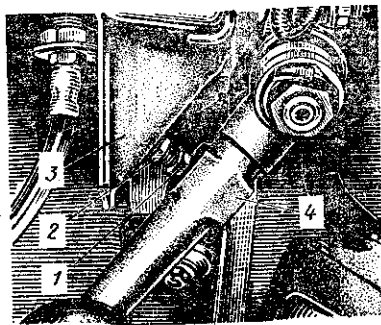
Узел регулировки максимального угла поворота переднего колеса: 1 — регулировочный болт; 2 — контргайка; 3 — кронштейн лонжерона рамы; 4 — рулевая сошка
